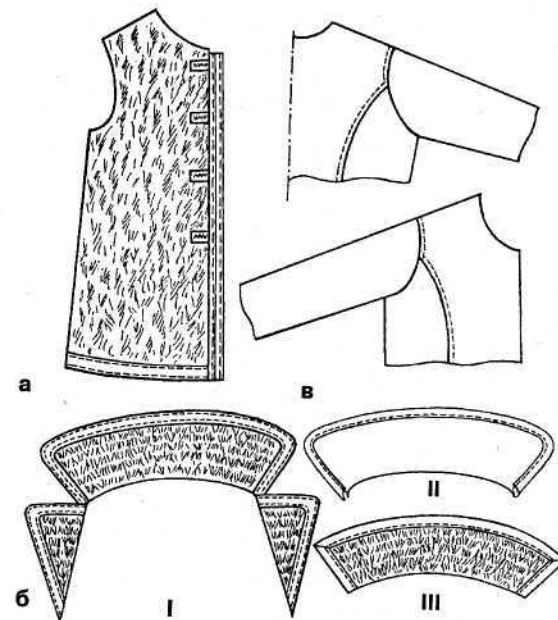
Особенности технологии изготовления одежды из шубной овчины
